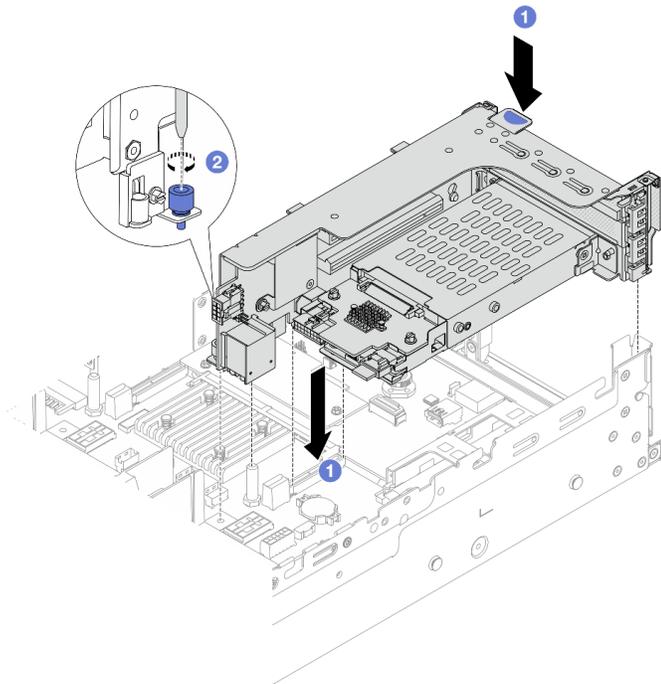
Installation d'un boîtier de carte mezzanine SSD 2FH + 7 mm
